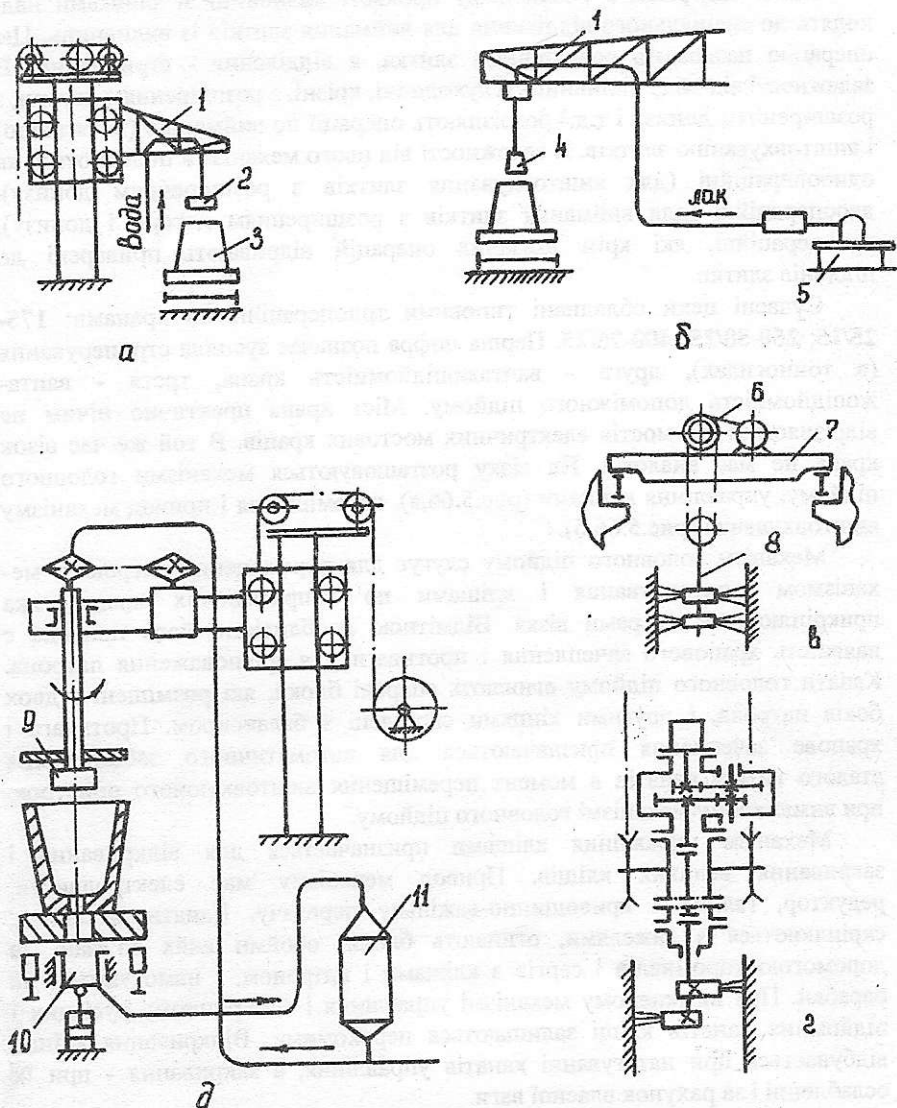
Схеми устаткування для чищення і змазування виливниць: а-гідралічна установка для чищення; б-установка для змазування; в-машина для механічного щіткового чищення; г-робочий щіточний орган; д-установка дробоструменевого чищення; 1, 6-механізм переміщення робочого органу; 2-голівка з форсунками; 3-виливниця; 4-розниловач; 5-напірна станція; 7-міст; 8-робочий орган; 9-дробострумнева голівка; 10-відсмоктуючий патрубок; 11-камера для подрібнення
